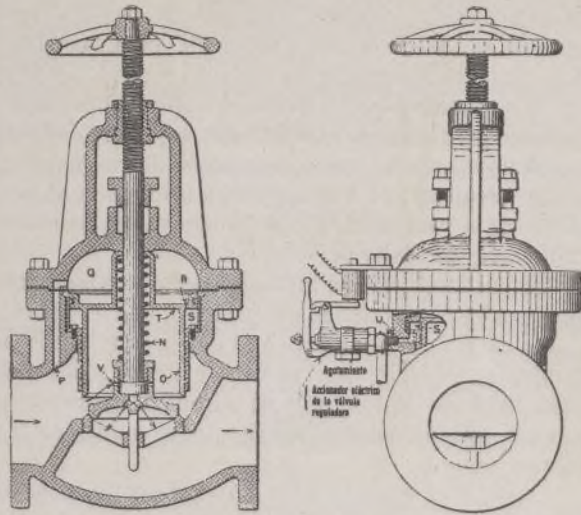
Válvula ahogadora y paro automático de la máquina.
